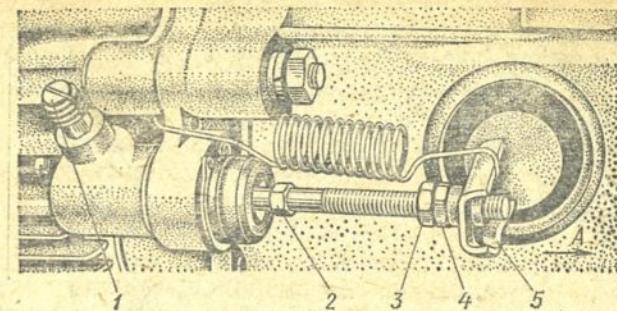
Регулировочный узел гидравлического привода сцепления:
